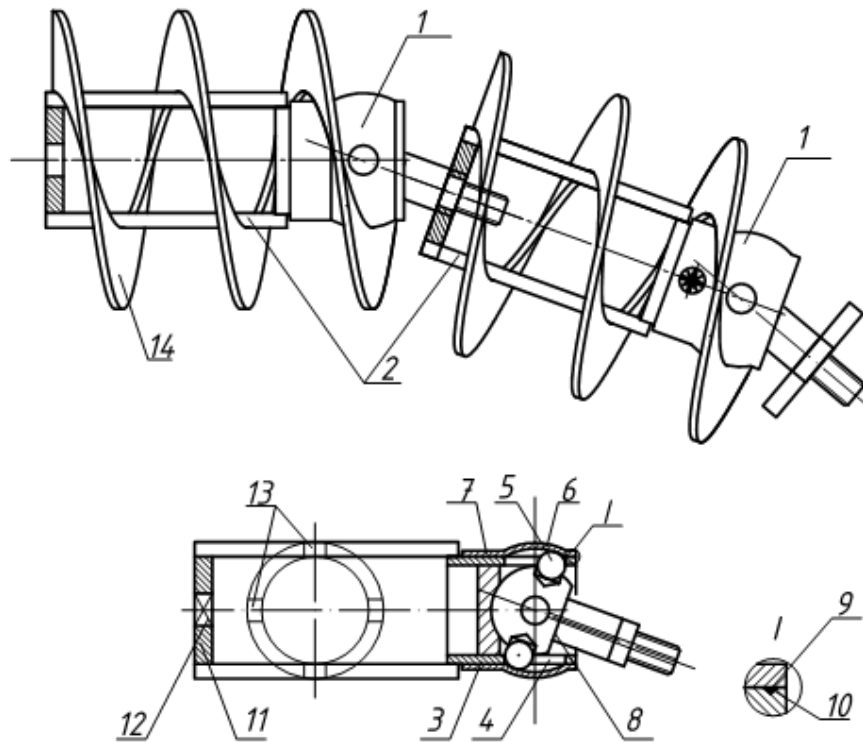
Гвинтовий секційно-шарнірний робочий орган
